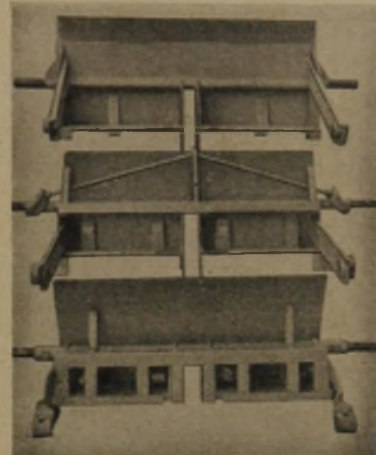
Entwicklung in der Bautechnik des Schwingkolbens einer Strohpresse (oben: geschweißte Stahlkonstruktion, Mitte: Schraub- und Nietkonstruktion, unten: Holzkonstruktion)
